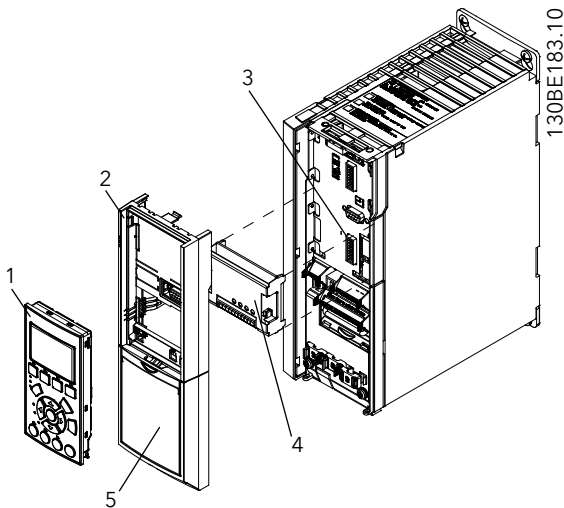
Установка корпусов размера A2, A3, B3, B4
